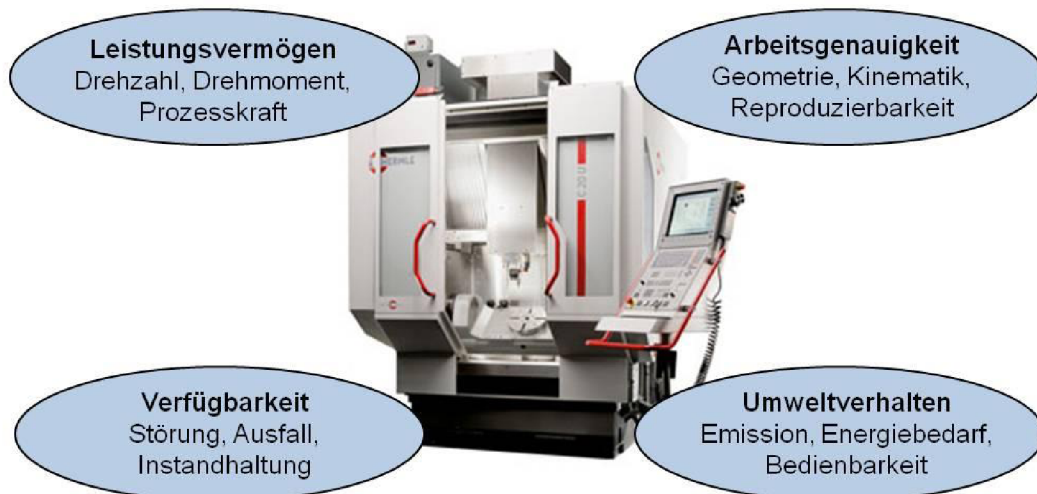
Eigenschaften der Werkzeugmaschine [7].
